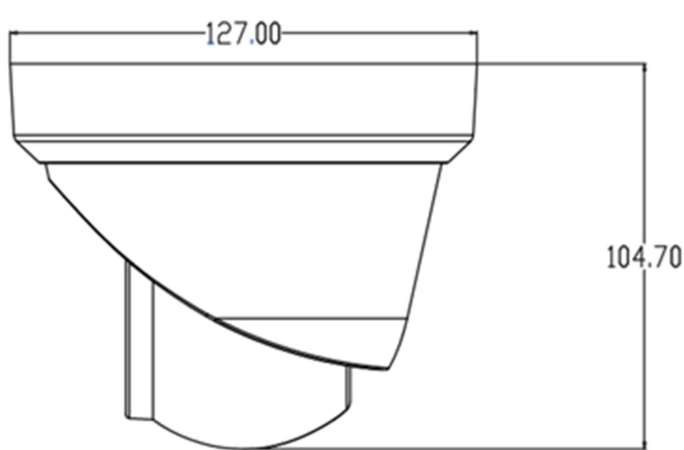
Габаритные и установочные размеры камер MD.
